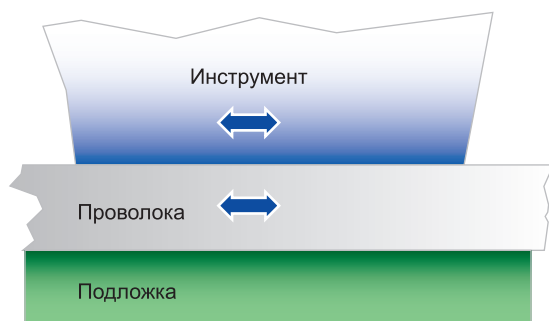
Первая стадия формирования сварочного соединения
